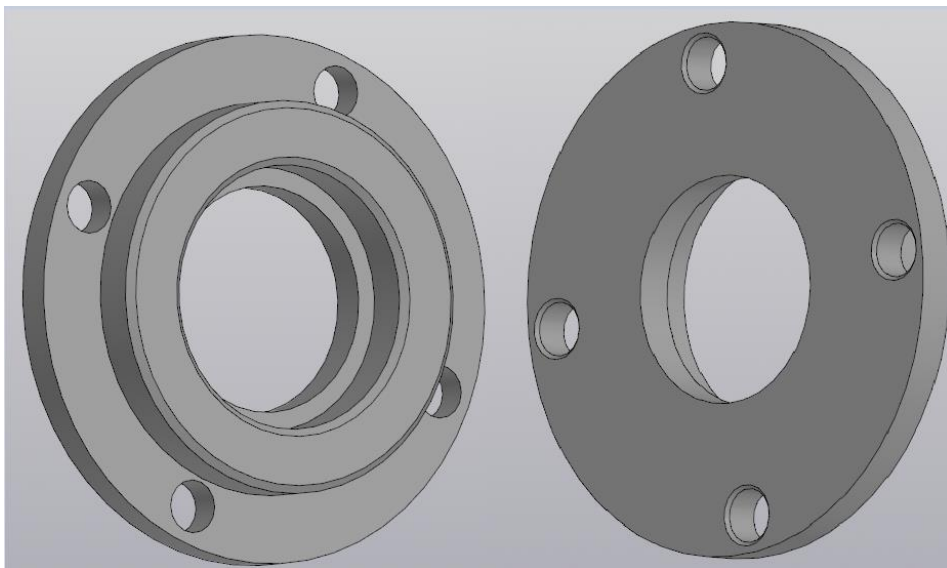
3D модель заготовки деталі “Кришка”
